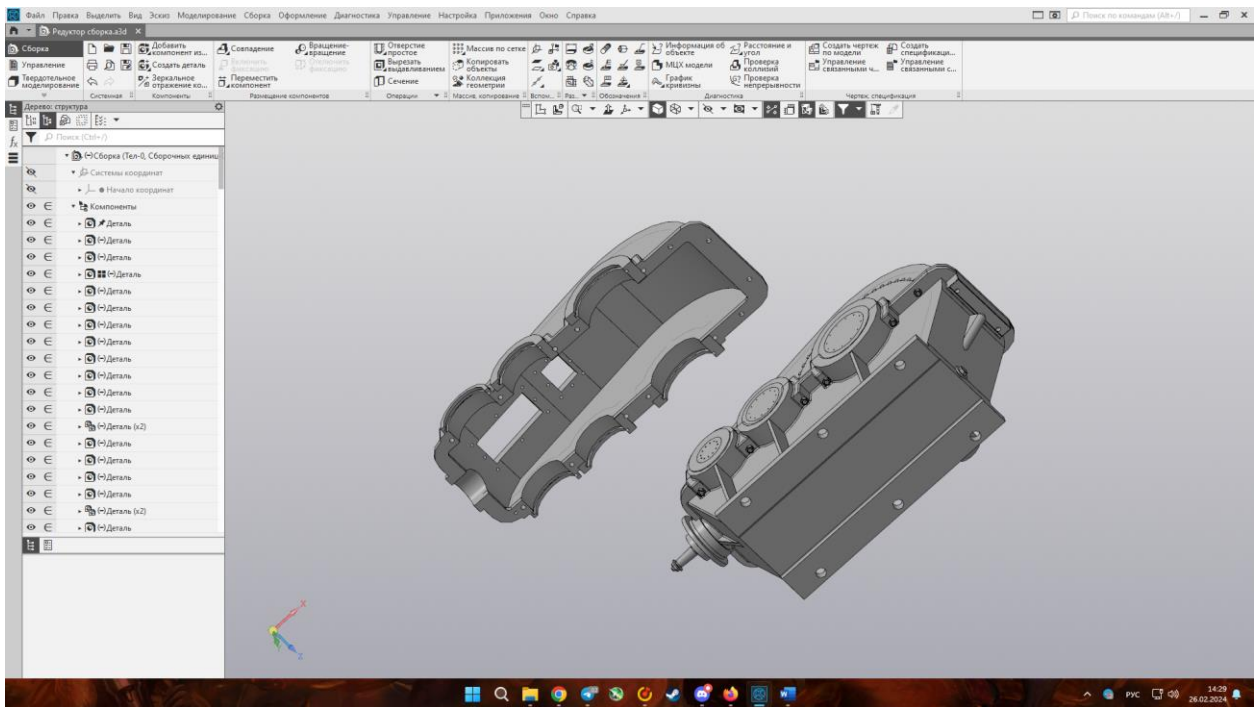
3D – модель верхней крышки и корпуса редуктора
